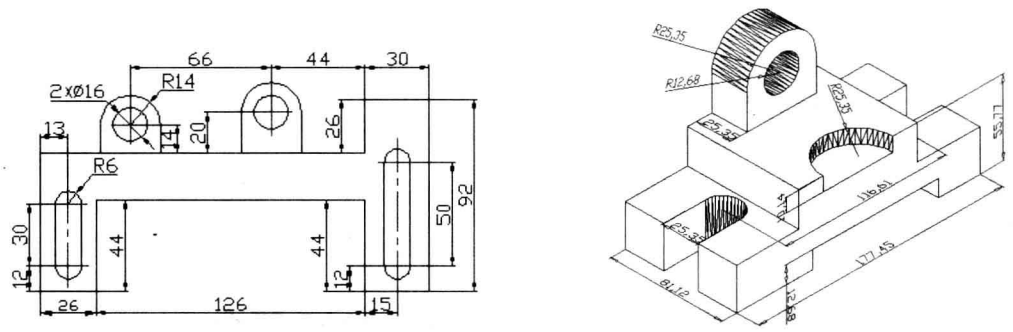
使用 AutoCAD 标注的平面和三维图形
